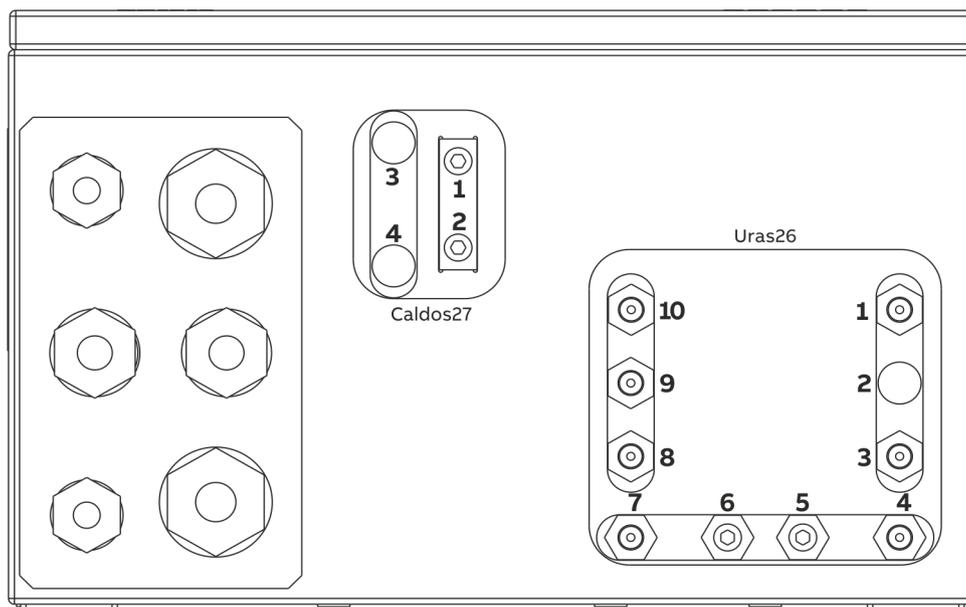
Gasanschlüsse Uras26 mit Caldos27 (Modell EL3040)
